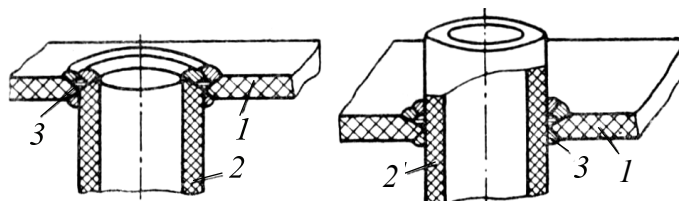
Пример сварного соединения плиты с трубой:
